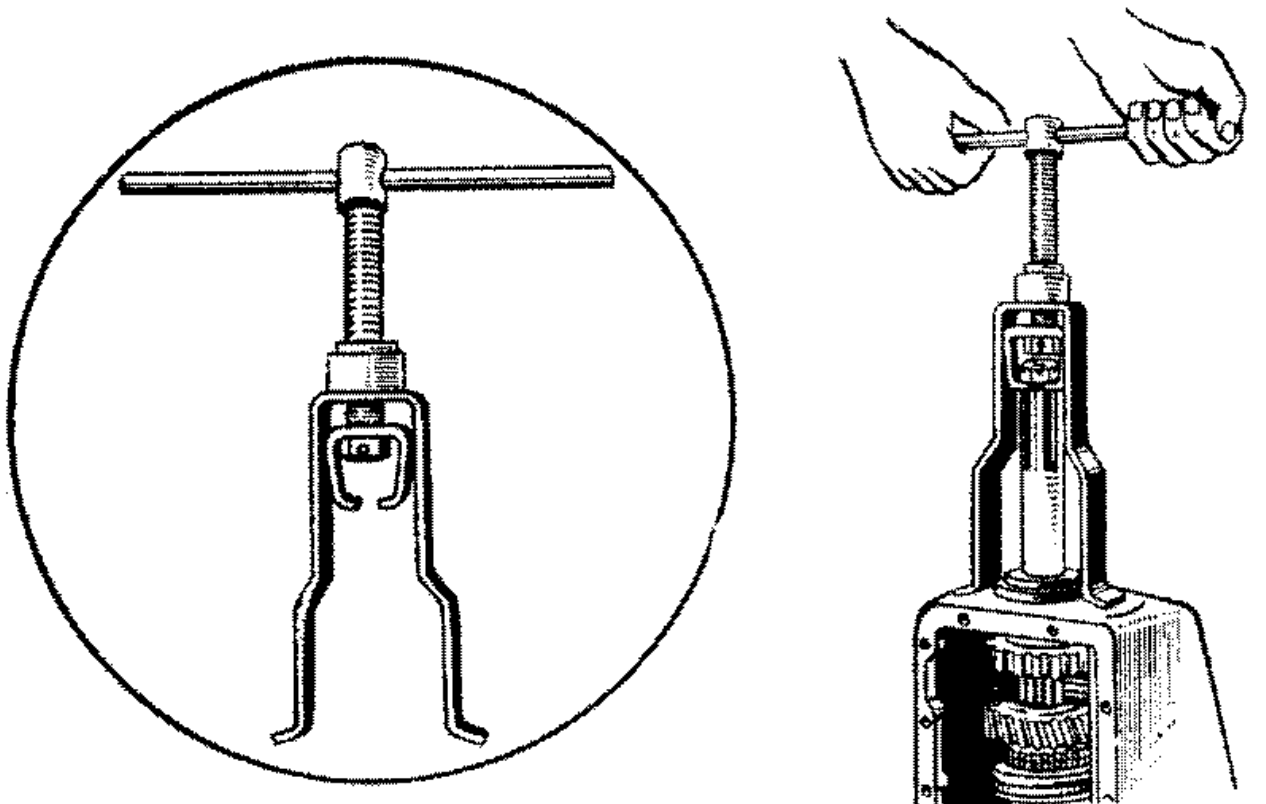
Выпрессовка подшипника ведомого вала из картера
